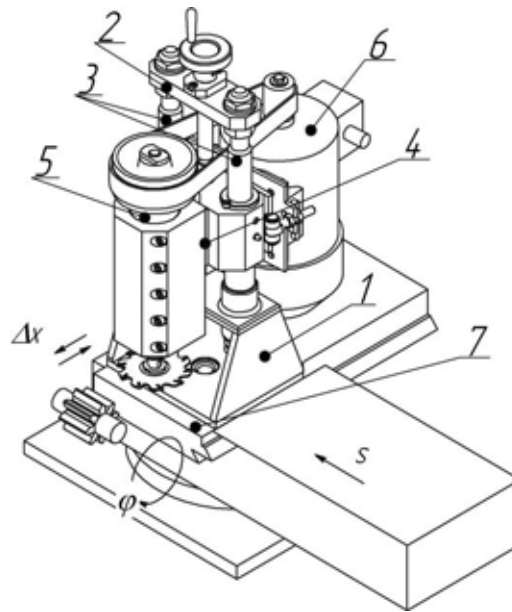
Конструкція пристосування для контурної обробки циліндричних зубчастих коліс на токарно-затилувальному верстаті
